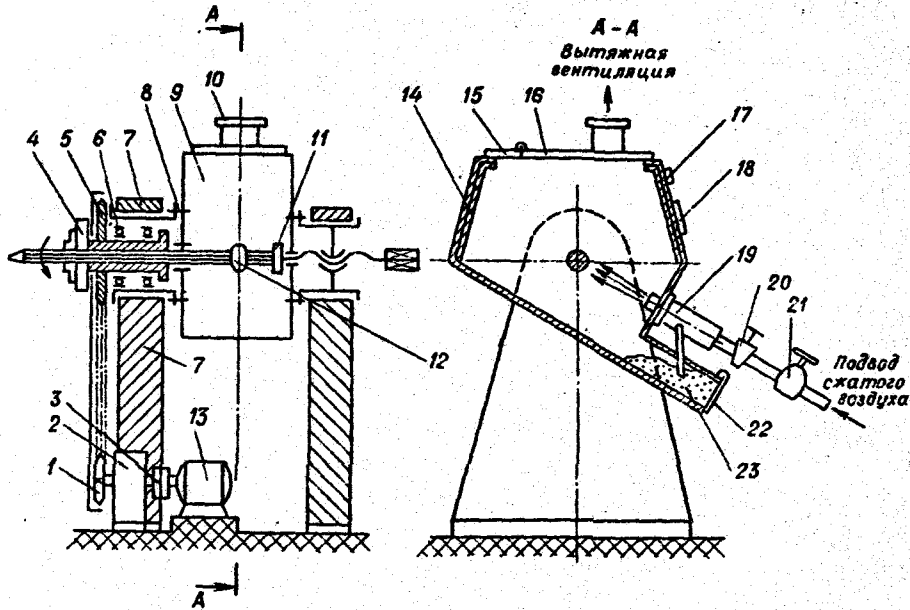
Схема дробеструйной установки для упрочнения буровых штанг
